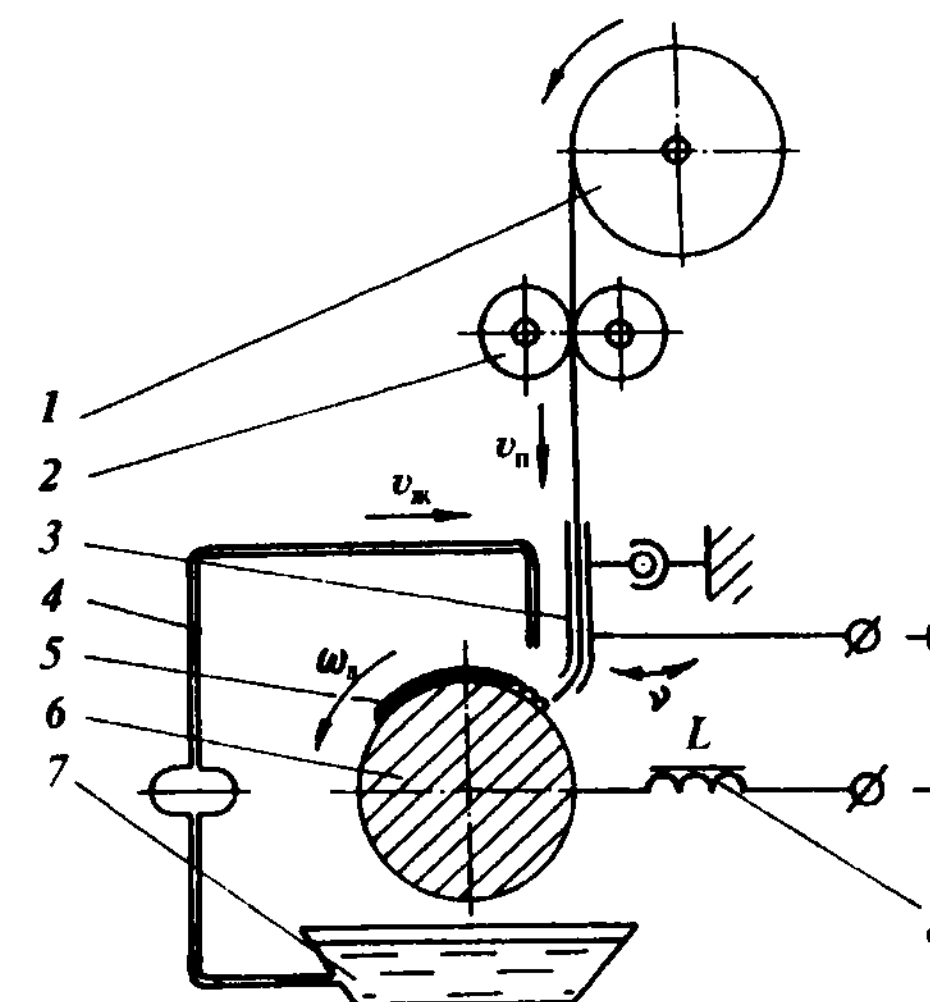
Схема вибродуговой наплавки: 1 – кассета для проволоки; 2 – подающие ролики; 3 – качающийся мундштук; 4 – система подачи раствора; 5 – наплавленный слой; 6 – восстанавливаемая деталь; 7 – емкость; 8 – индуктивное сопротивление; v_p и $v_{ж}$ – скорость подачи соответственно проволоки и раствора; ω_d – угловая частота вращения детали; v – частота качаний мундштука; L – индуктивность
